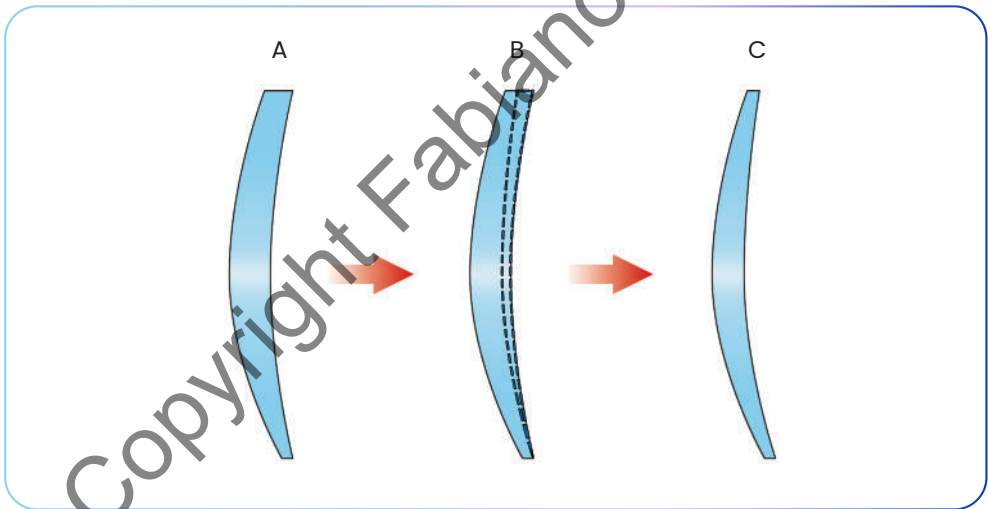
Fasi di realizzazione del prisma di alleggerimento nelle L.P.
